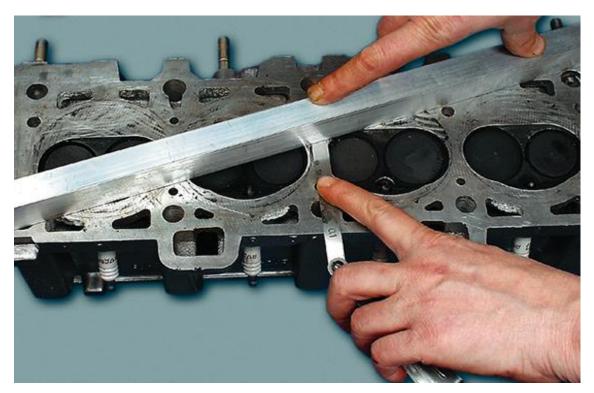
Проверка деформации привалочной плоскости головки блока цилиндров
